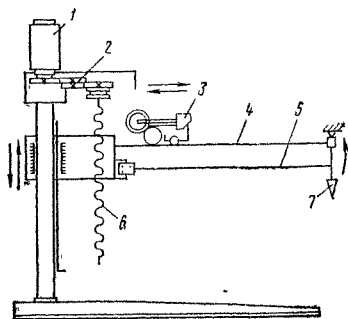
Кинематическая схема установки ВМС-121М для автоматической сварки воздуховодов
